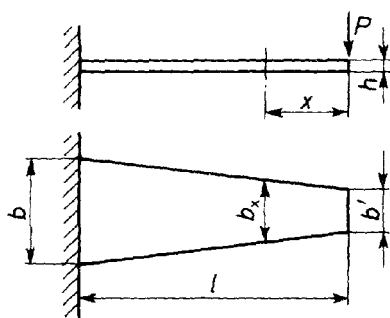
Molla a lama piana a pianta trapezoidale.
